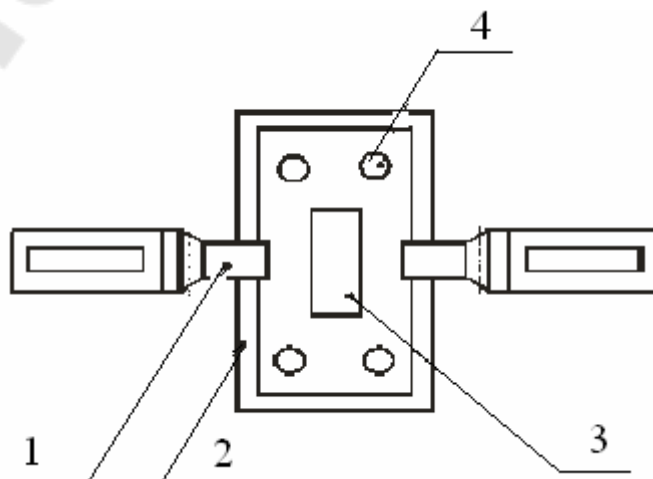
Схема ультразвукового упрочнения шариками: 1 – волновод; 2 – камера; 3 – обрабатываемая деталь; 4 – стальные шарики
